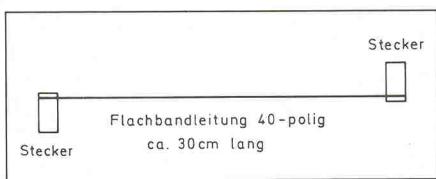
So müssen die Stecker auf die Flachbandleitung gepreßt werden.
